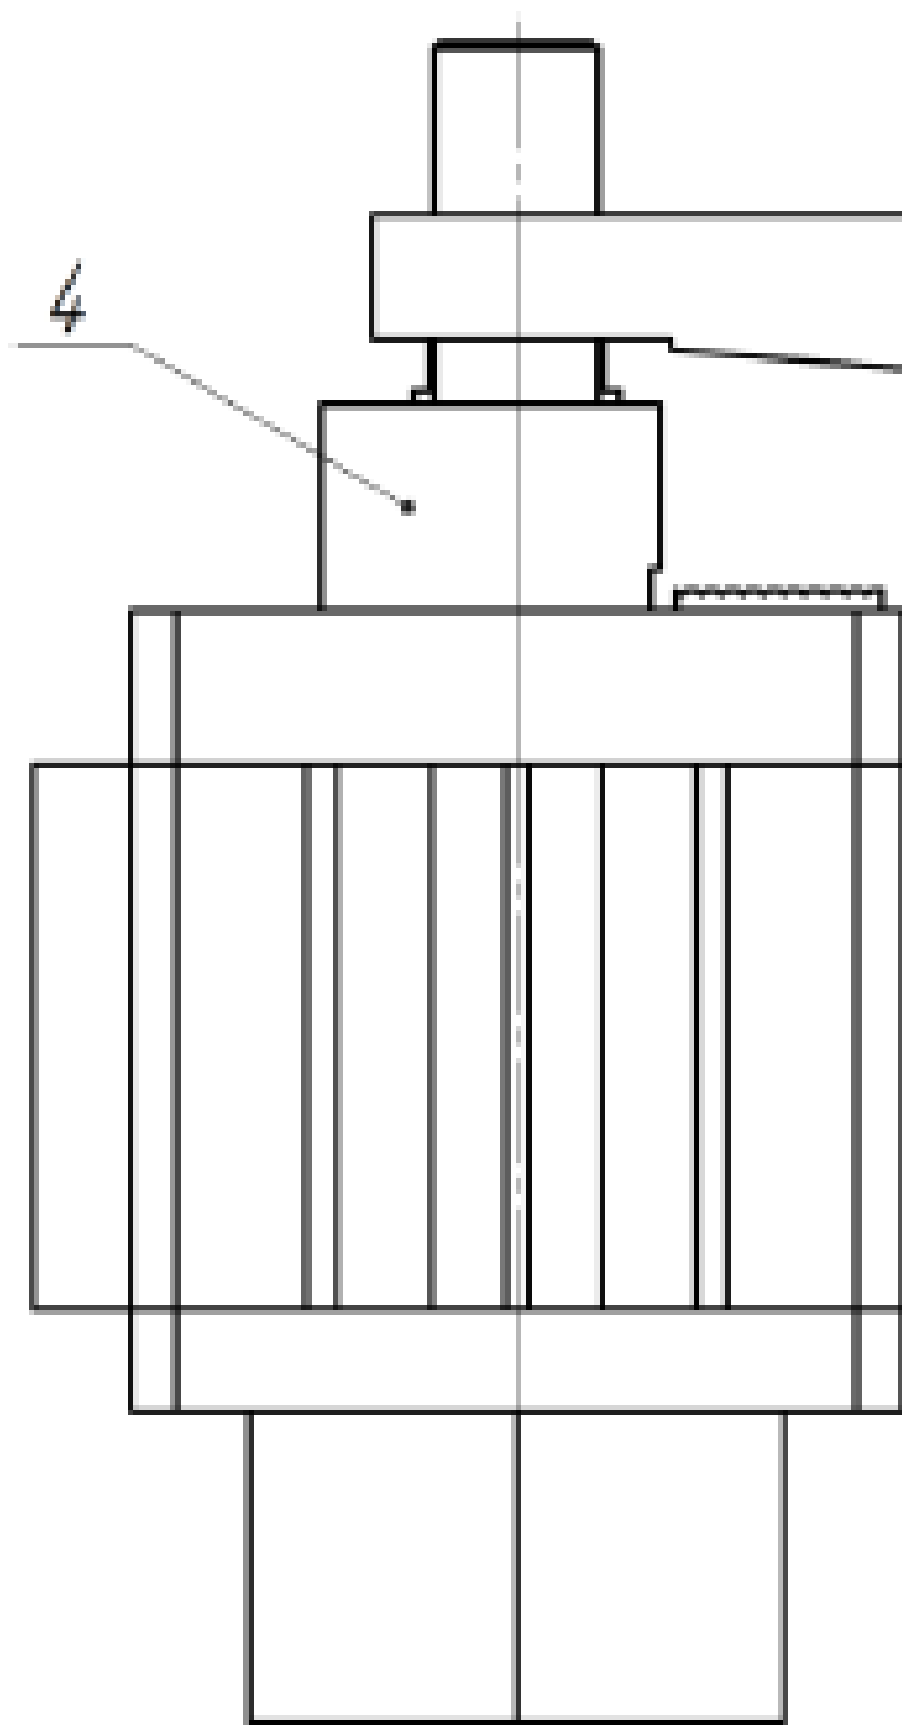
Конструктивні елементи автоматизованого верстатного пристрою, вигляд зліва [204]
